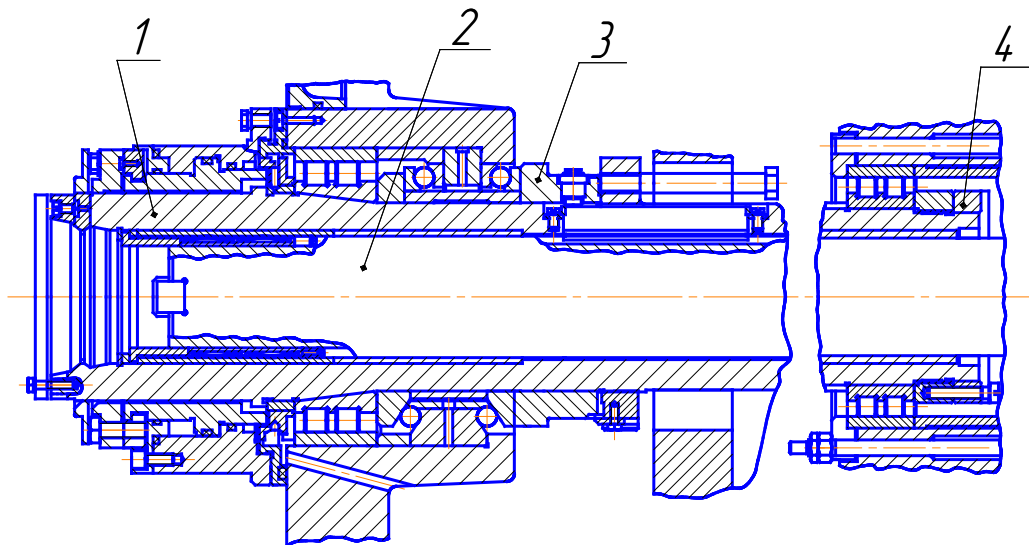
Шпиндельний вузол верстата 2A622-МФ2
